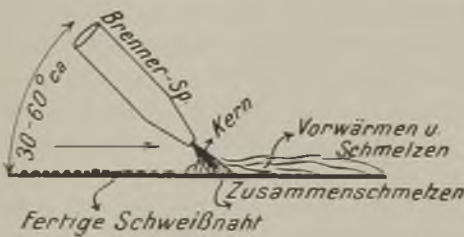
Richtige Haltung des Brenners beim Schweißen.
